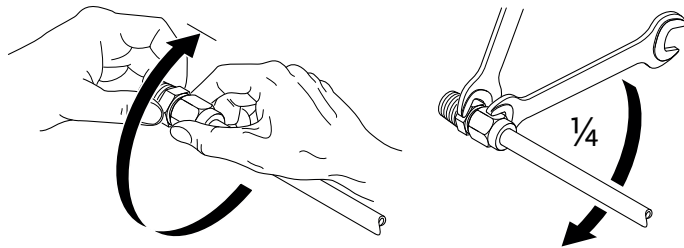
Дополнительный поворот резьбового соединения с обжимным кольцом на 1/4 оборота
